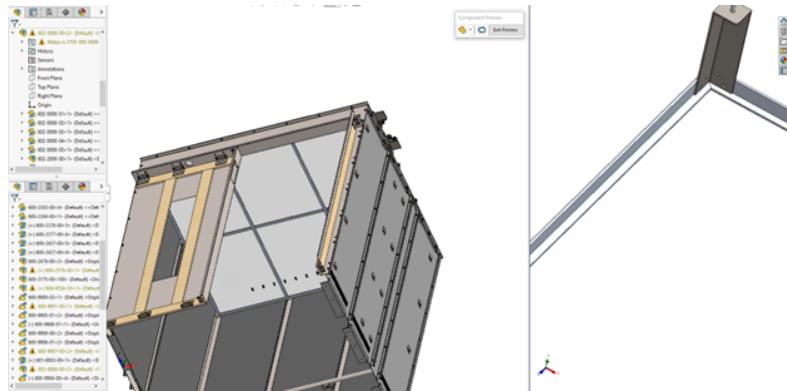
De esta manera se pueden hacer mates en partes difíciles de accesar
